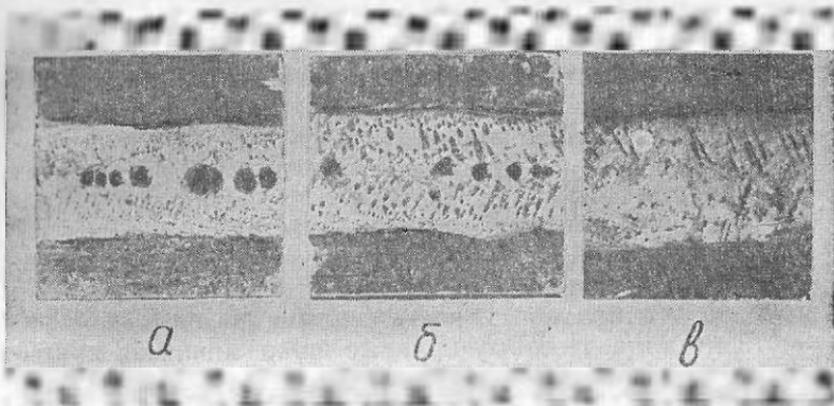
Влияние скорости сварки на пористость швов при автоматической сварке под влажным флюсом на различных скоростях: а — 24 м/ч; б — 17 м/ч; в — 12 м/ч
